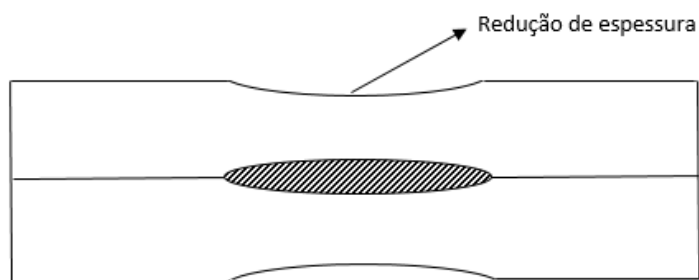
Esquema do efeito de redução de espessura na soldadura por roletes.
